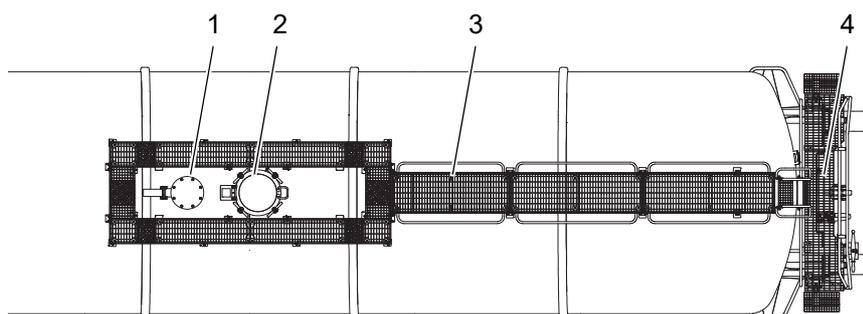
Obere Befüll- und Entleereinrichtungen, Standardausstattung
